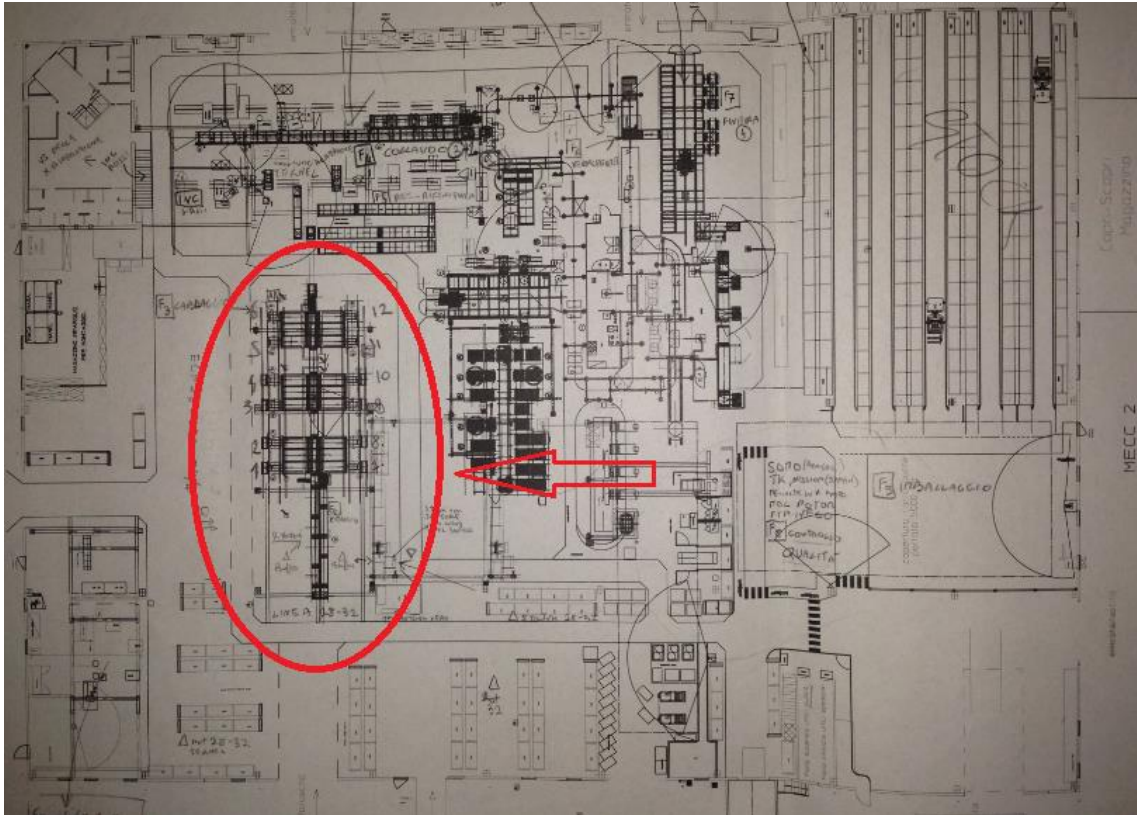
, Layout Mecc2 con evidenza Linea Cassioli 28-32
